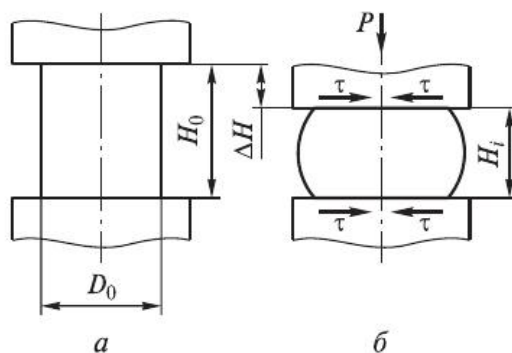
Схема осадки (сжатия) цилиндрической заготовки:
